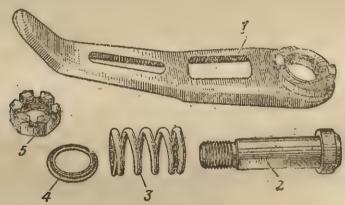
Зажим ноги: 1 — рычаг; 2 — болт; 3 — пружина; 4 — шайба; 5 — гайка
